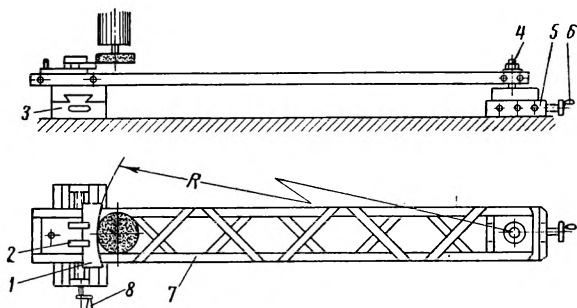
Приспособления для шлифования вогнутых цилиндрических поверхностей
